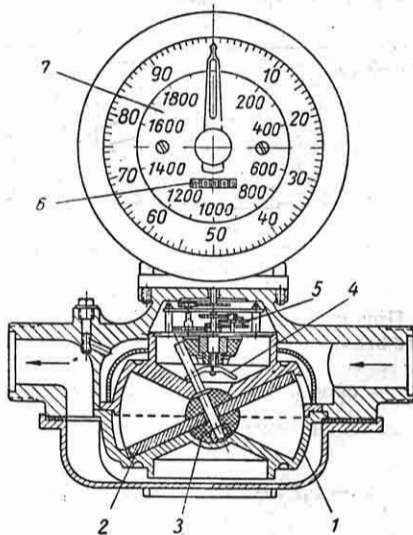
Схема расходомера-счетчика с нормальной осью: 1 — корпус; 2 — головка; 3 — крыльчатка; 4 — шип; 5 — передаточный механизм (редуктор); 6 — герметичная перегородка; 7 — счетный механизм; 8 — сетка (фильтр).
